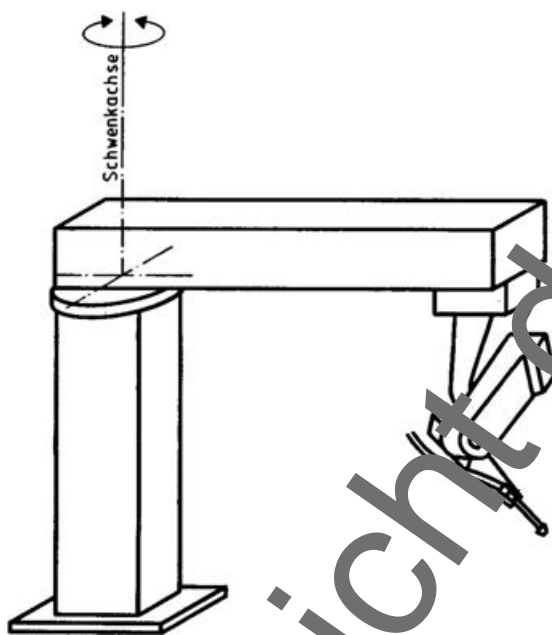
Roboterpositionierer mit einer rotatorischen Achse.
